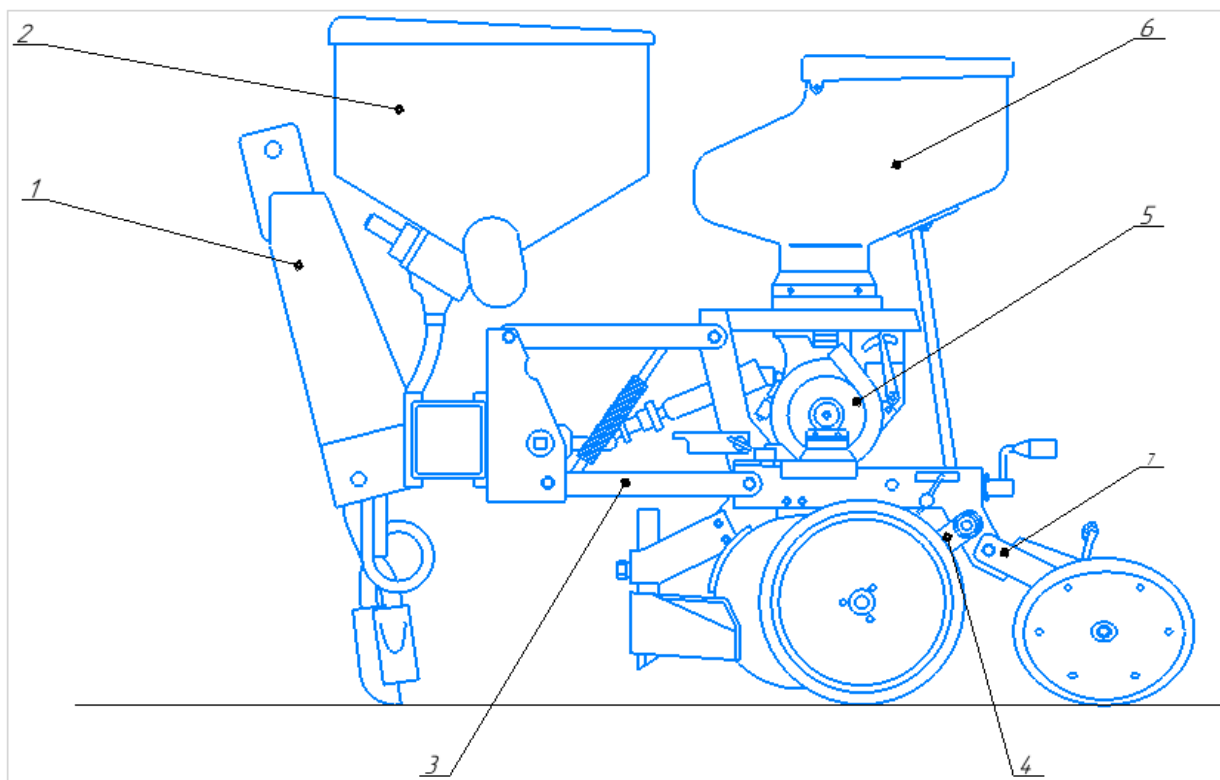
Загальний вигляд сівалки Maschio Gaspardo MT-8: 1 – начіпний пристрій; 2 – бункер для добрив; 3 – механізм копіювання поверхні ґрунту; 4 – важіль з опорним колесом сошника; 5 – висівний механізм; 6 – бункер для насіння; 7 – прикочуючий механізм
